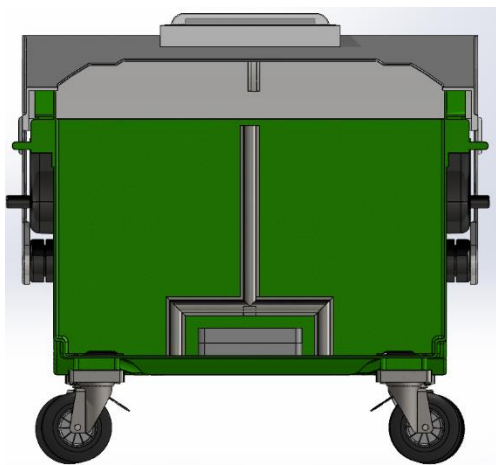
Modelação em ambiente SolidWorks – Montagem final - Vista em corte frontal
